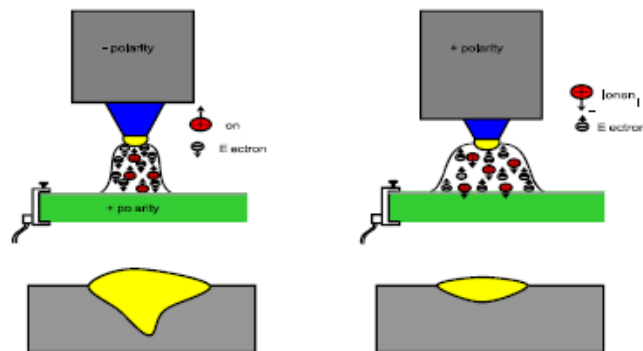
Penetración de la soldadura y flujo de electrones en función de la polaridad de soldadura.
